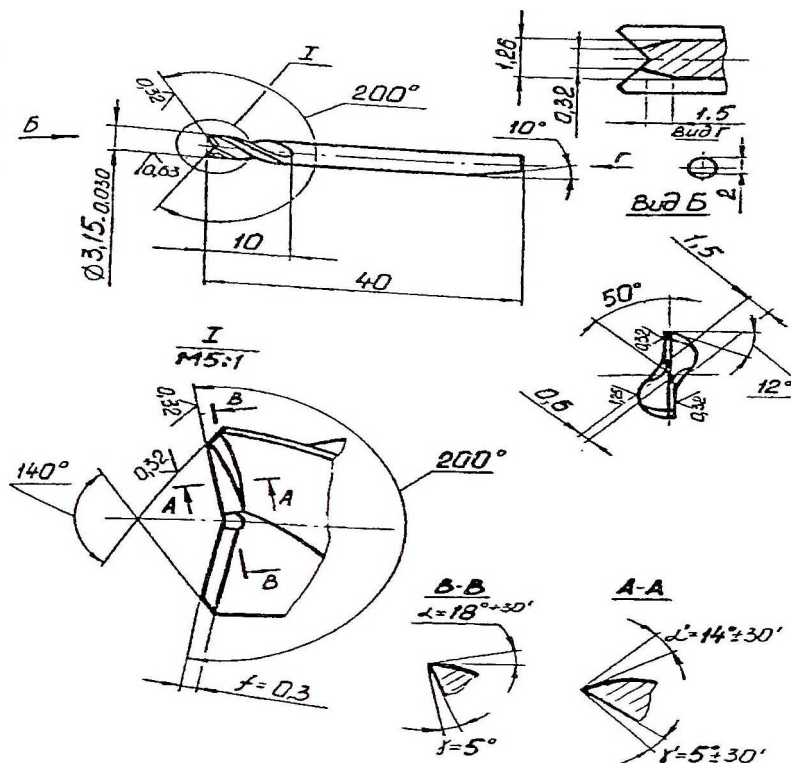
Конструкция и геометрия заточки спирального сверла с обратным заборным конусом
